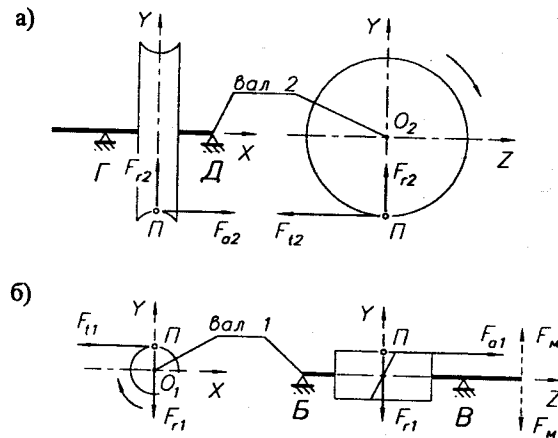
Схемы сил F_t , F_r и F_o , нагружающих валы: а) червячного колеса (вал 2); б) червяка (вал 1)
